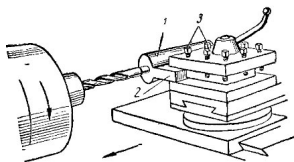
Приспособление для закрепления сверла в резцержателе (по предложению токаря Л. Я. Мехонцева)
